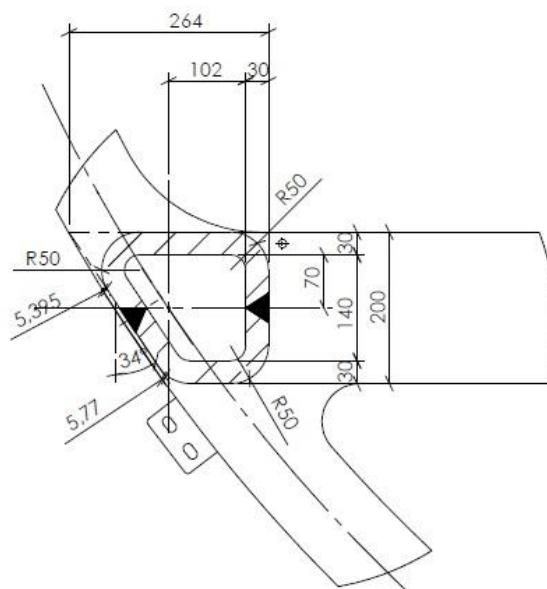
Secção transversal das vigas longitudinais [24]
